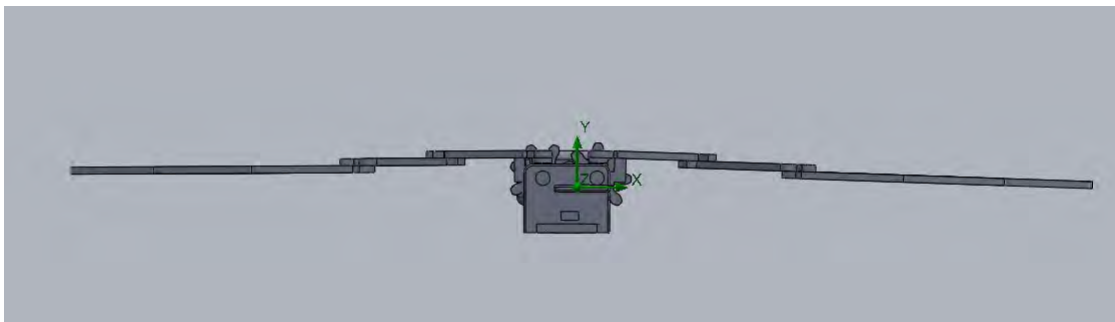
Vista frontal del ensamblaje en SolidWorks.
